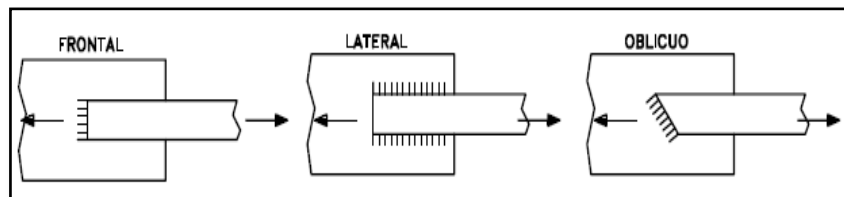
Cordones de soldadura respecto al esfuerzo
